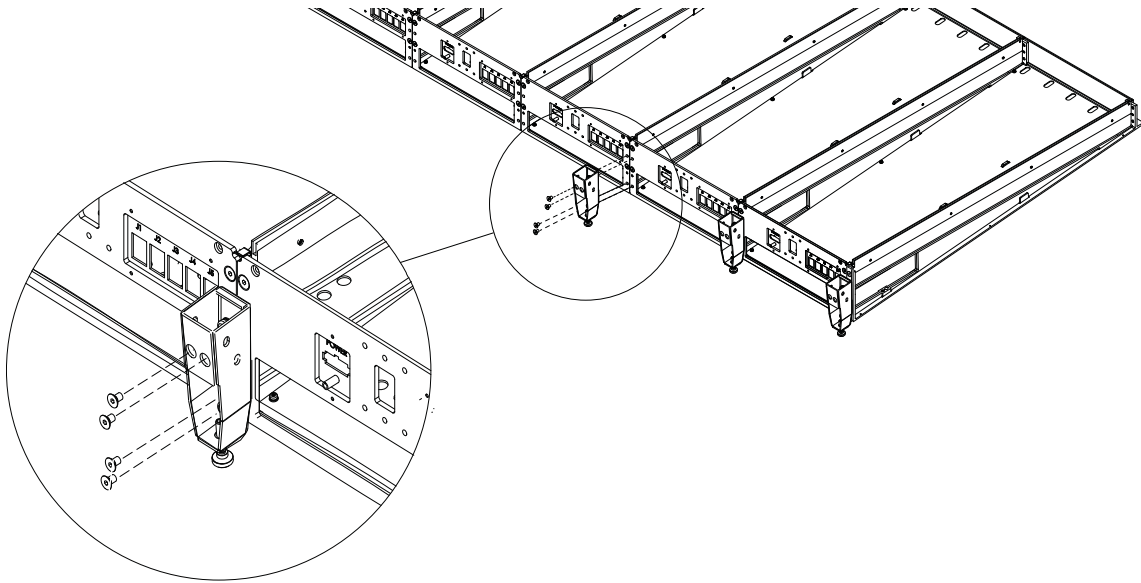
Fixation d'un pied arrière à deux plaques de connexion arrière adjacentes
